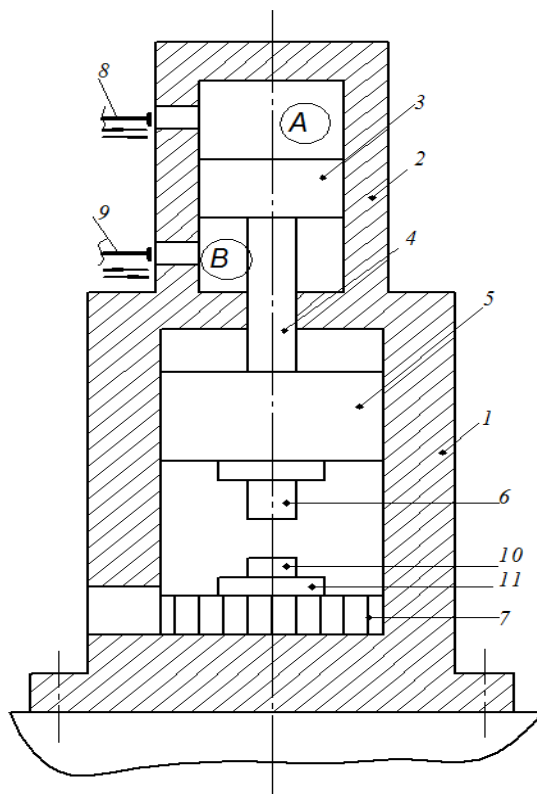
Конструкция гидропресса с вращающимся штамподержателем
